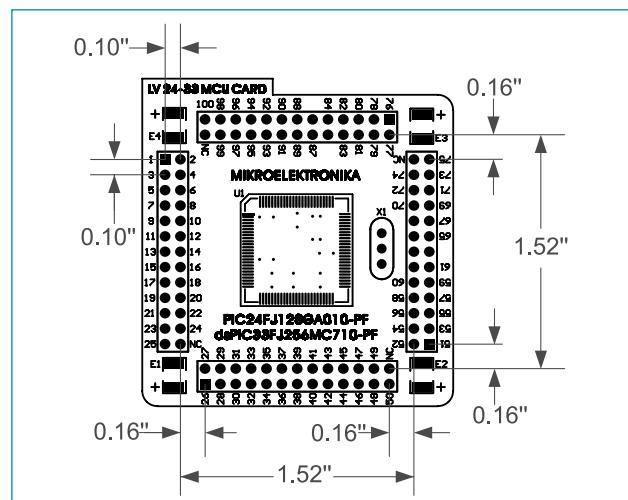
Dimensiones de la tarjeta MCU para las MCU Card 1 a MCU Card 8
